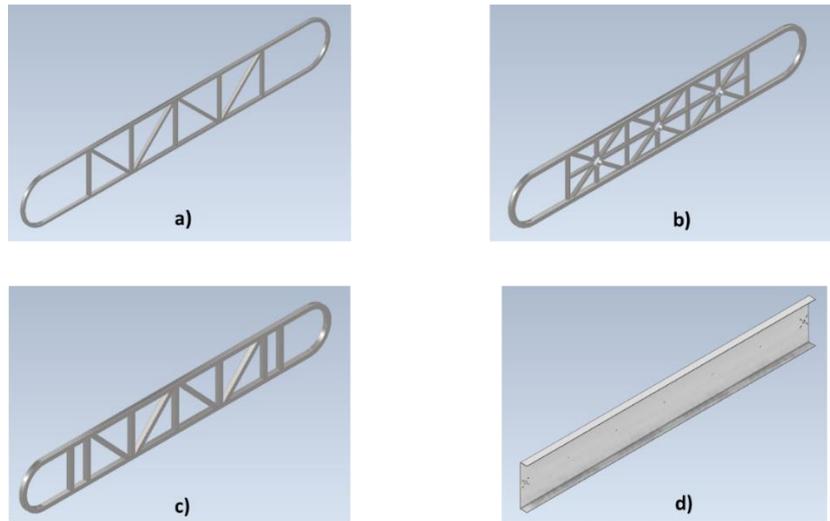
Estructuras propuestas. a) Diseño Warren perfil delgado. b) Diseño para travesaños tubulados. c) Diseño Warren reforzado. d) Viga como estructura. Elaboración propia.
